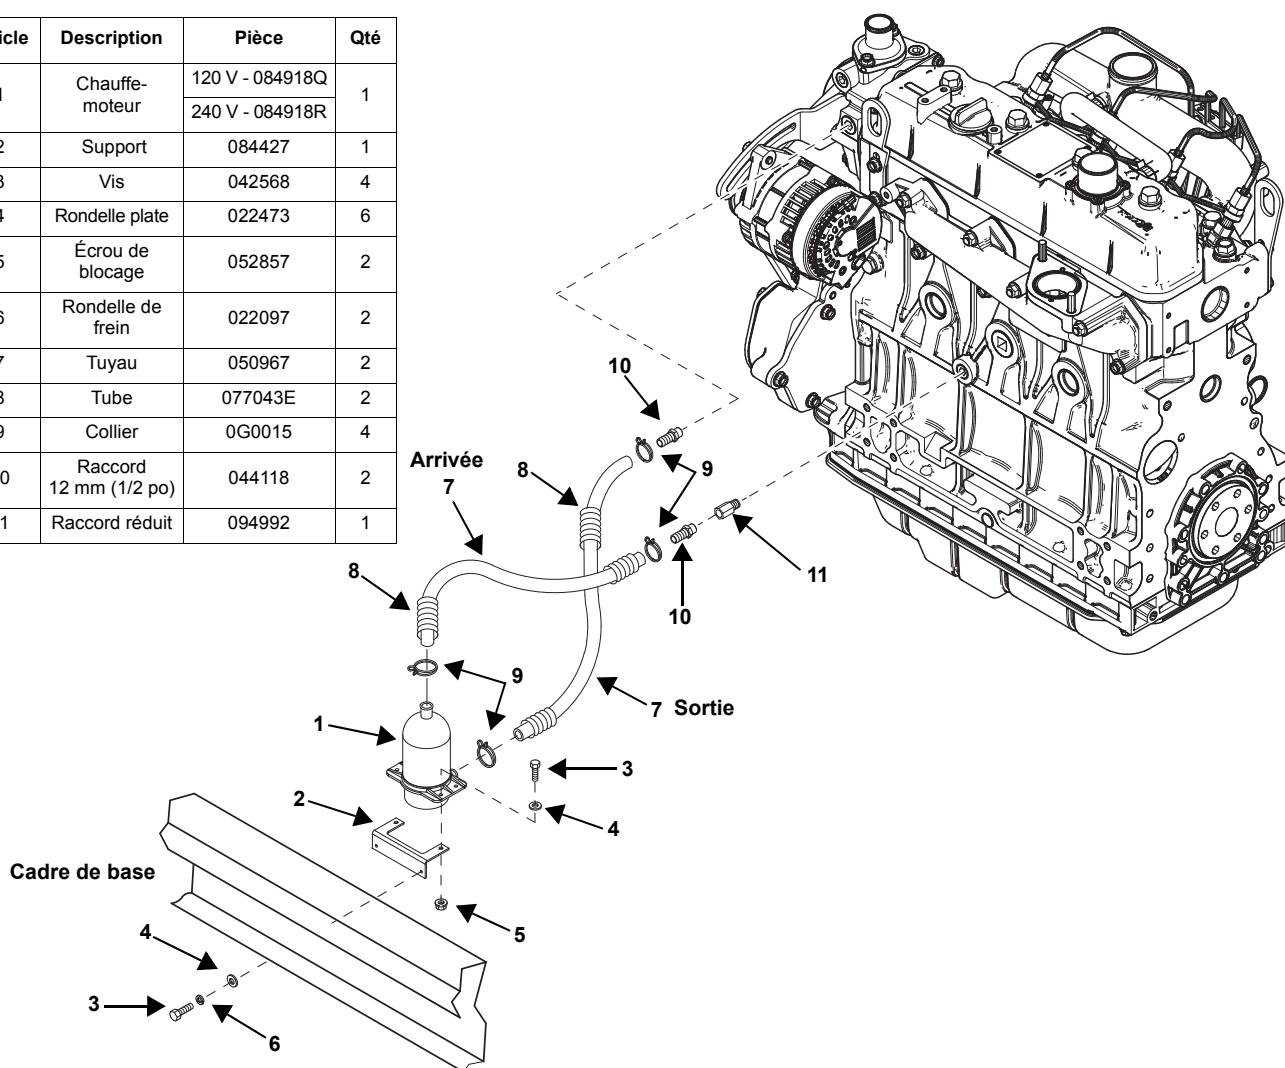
Assemblage du chauffe-moteur (vue éclatée — Modèles 2,3 L)
